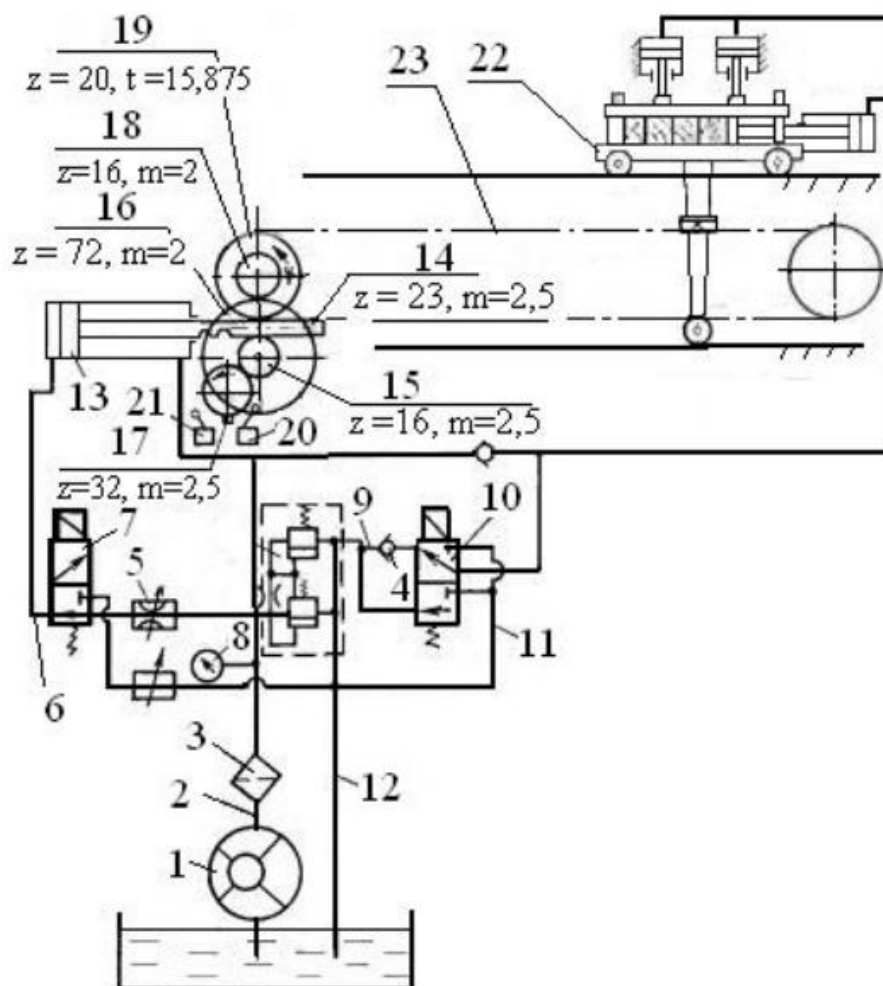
Гидрокинематическая схема привода каретки станка ШО15Г
